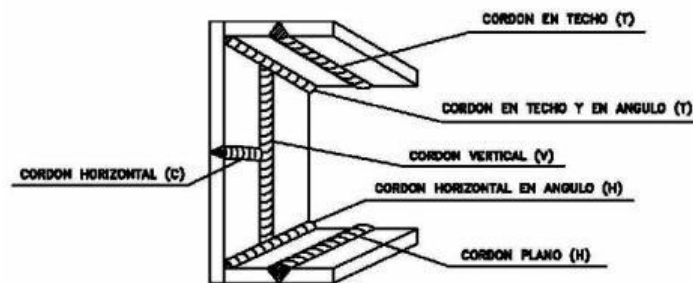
Tipos de soldadura por el tipo de posición.
